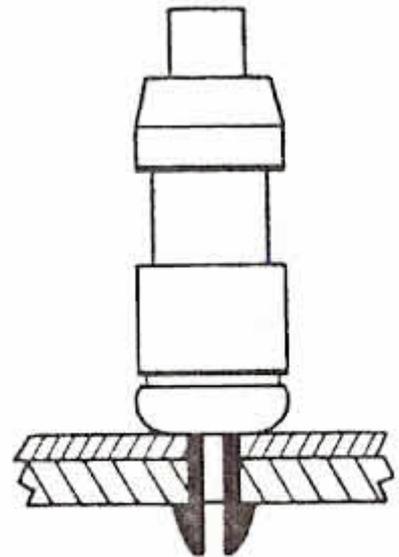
Disposición del sujetador Wedgelock adaptado a un taladro
